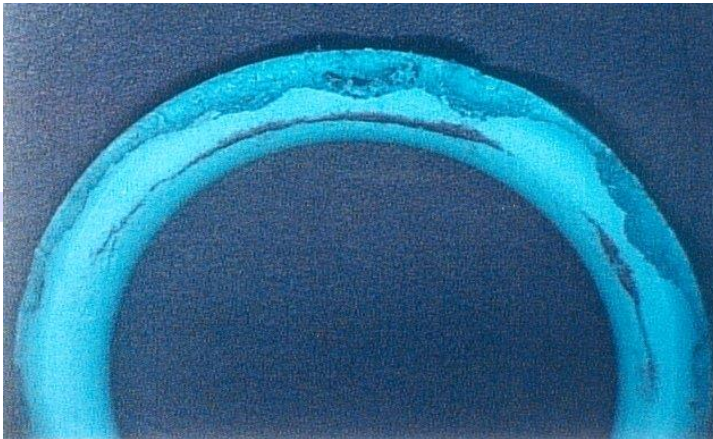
Geschädigter O-Ring durch Spaltextrusion: Die Ausbrüche ähneln dem Schadensbild einer Explosiven Dekompression
